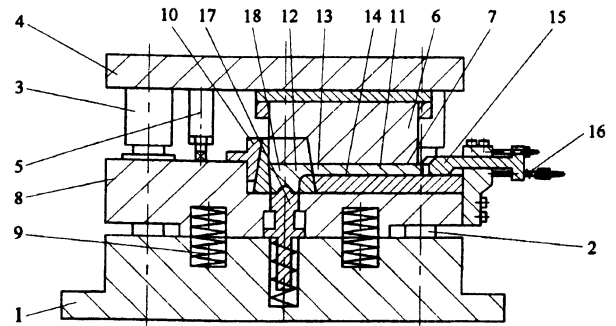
Специальный штамп для изготовления поковок шатунов для велосипедов: 1 — нижняя плита; 2 — колонка; 3 — втулка; 4 — верхняя плита; 5 — регулируемый упор; 6 — пуансон; 7 — плоская площадка; 8 — промежуточная плита; 9 — пружина; 10 — матрица; 11 — штамповочный ручей смешанного вида; 12 — закрытая формовочная полость; 13 — открытый участок; 14 — плоская площадка; 15 — призма; 16 — пружина; 17 — выталкиватель; 18 — шатун велосипеда
